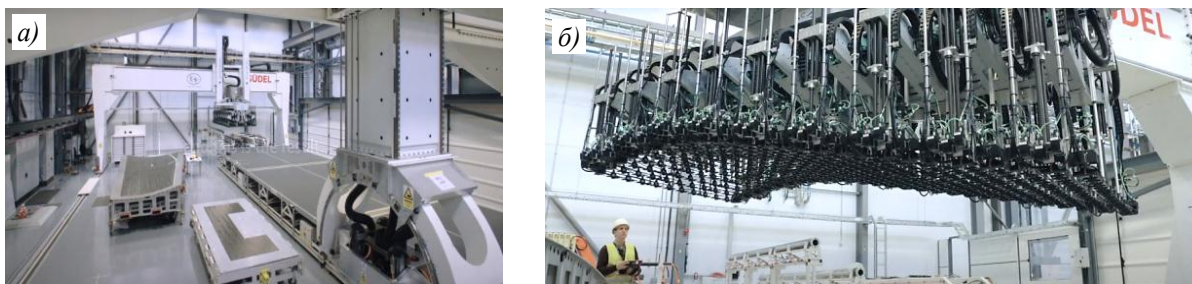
Роботизированный комплекс Güdel: общий вид (а), а также захват раскрытой заготовки с помощью манипулятора с 270 вакуумными присосками и перенос ее на форму (б)
